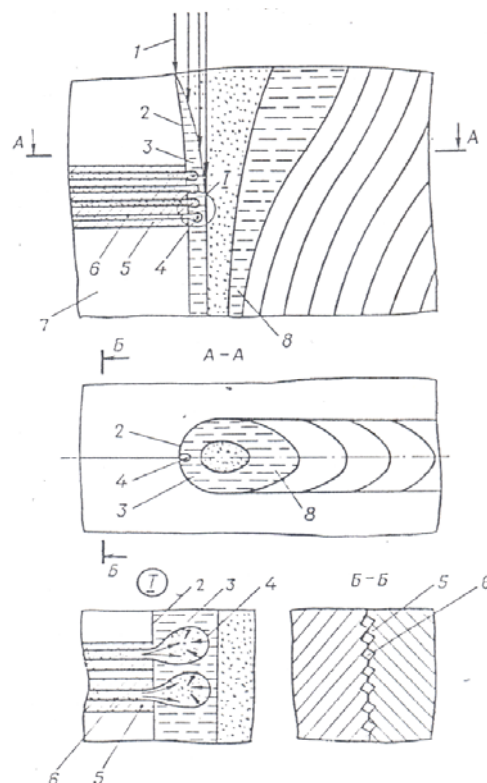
Механизм образования газовых пузырьков в передней части сварочной ванны: 1 – электронный луч; 2 – фронт плавления; 3 – передняя часть сварочной ванны; 4 – газовый пузырек; 5,6 – выступ и впадина на торцевой поверхности стыка; 7 – торцевая поверхность стыка; 8 – хвостовая часть сварочной ванны
